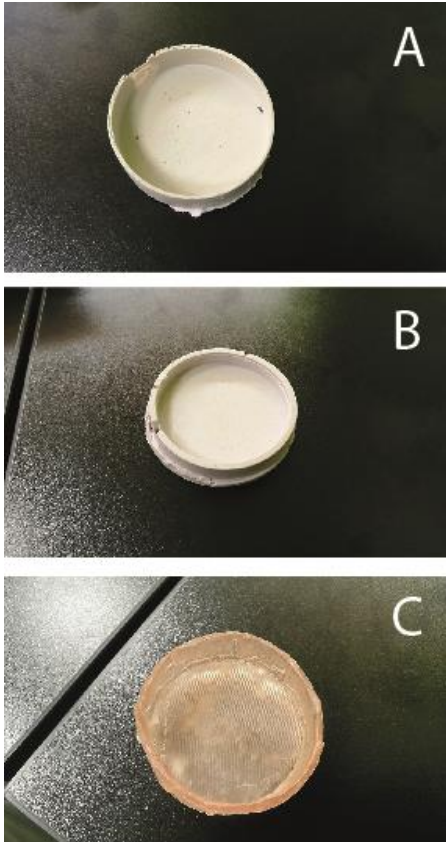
Molde hecho a partir de masilla mágica (A), molde hecho a partir de masilla mágica y resina de poliéster (B) y molde hecho con resina de poliéster solamente.
